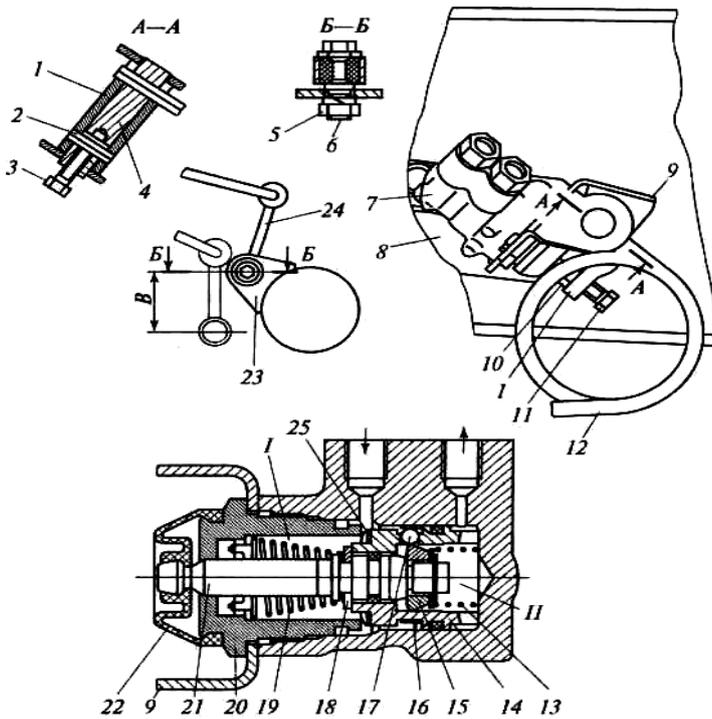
Регулятор давления: 1-нажимной рычаг; 2 — штифт; 3 — фиксирующий болт; 4 — ось нажимного рычага; 5 — гайка; 6 — ось; 7 — корпус; 8, 9 — кронштейны регулятора; 10 — контргайка; 11 — регулировочный болт; 12 — ; 13 — пружина; 14 — гильза поршня; 15 — управляющий конус; 16 — прижимная пружина; 17 — ; 18 — упорная скоба; 19 — возвратная пружина; 20- втулка; 21 — ; 22 — защитный чехол; 23 — кронштейн моста; 24 - стойка; 25 — пружинная шайба; В = 28 - 32 мм (для автобусов), В = 13 - 17 мм (для автомобилей)
